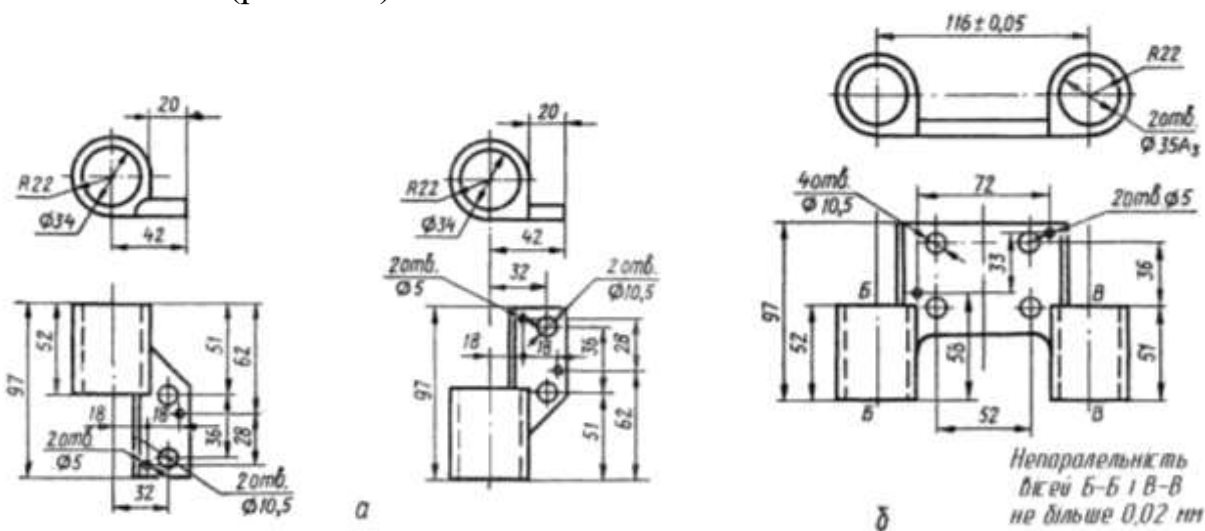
Приклад суміщеного штампування заготовки
